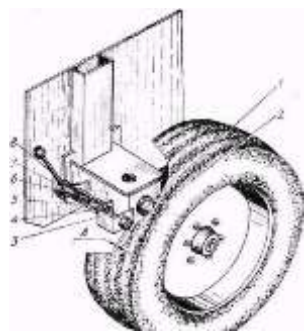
Тормоз колеса; 1 - шток; 2 - болт ступица колеса; 3, 5, 6 - пружина; 4 - труба тормоза; 7 - шайба; 8 - рукоятка. А = 3 - 5 мм
